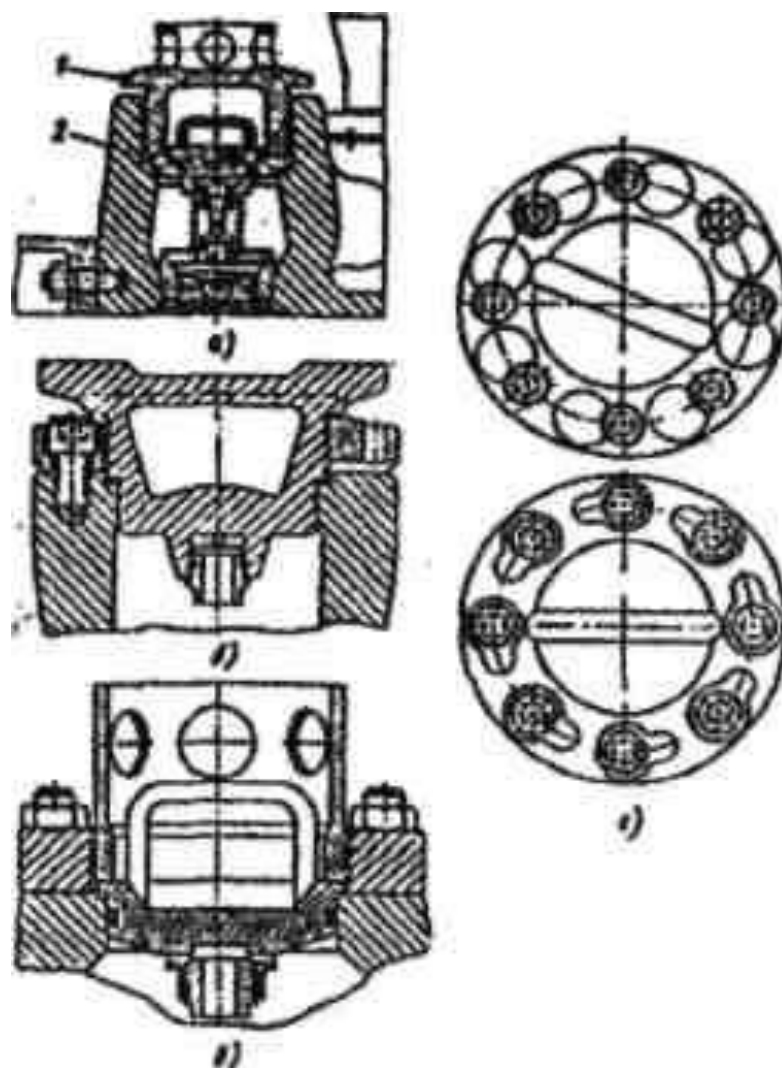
Крышки гидравлической коробки: а - закрепленная втулкой, ввернутой в корпус; б - ввернутая на резьбе во фланец и уплотненная плоской прокладкой; в - с втулкой, ввернутой на резьбе с уплотнительным кольцом круглого сечения; г - с фланцевым быстроразборным соединением
